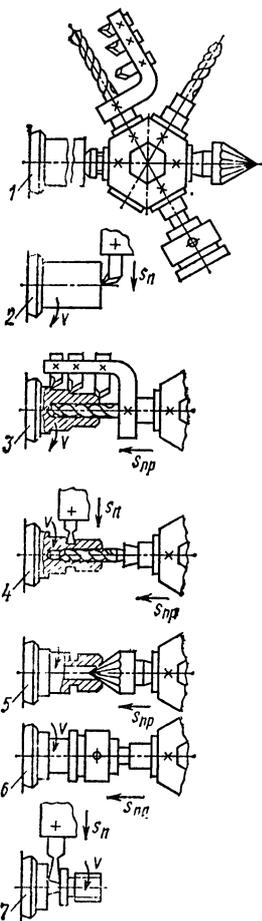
Схемы обработки заготовки на токарно-револьверном станке:
